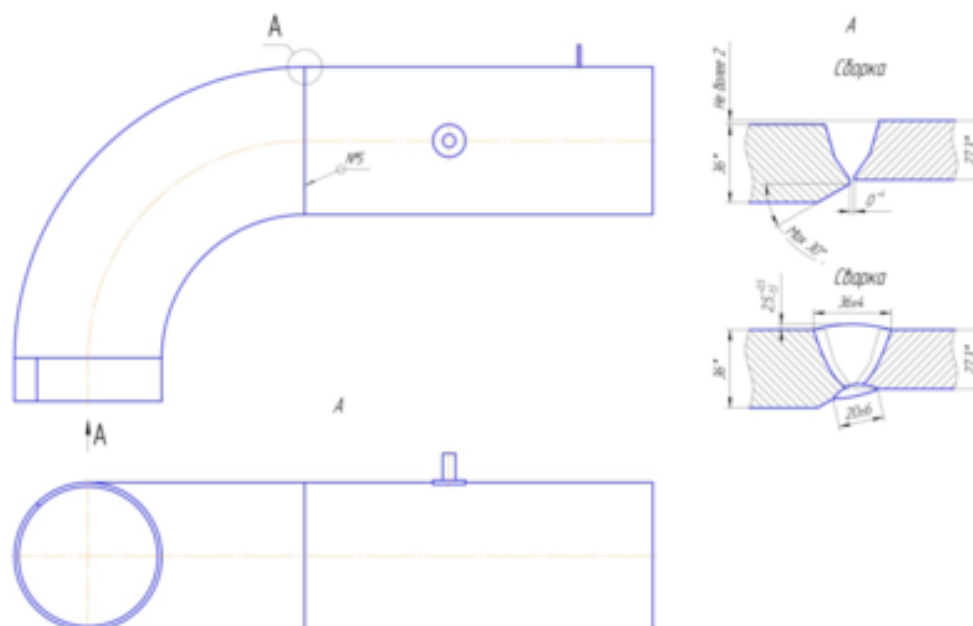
Схема сборки и сварки отвода с катушкой
